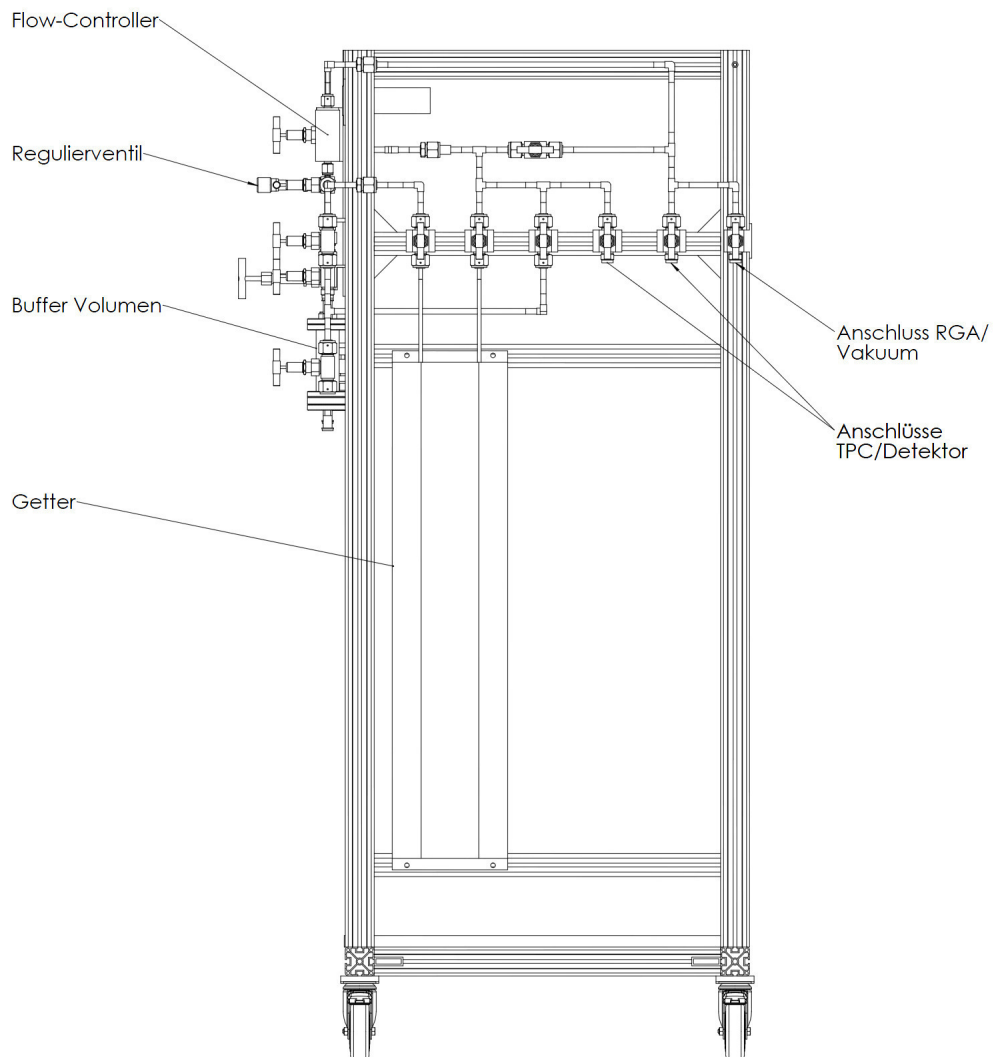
Seitenansicht des Gassystems mit Bezeichnung der Komponenten.
